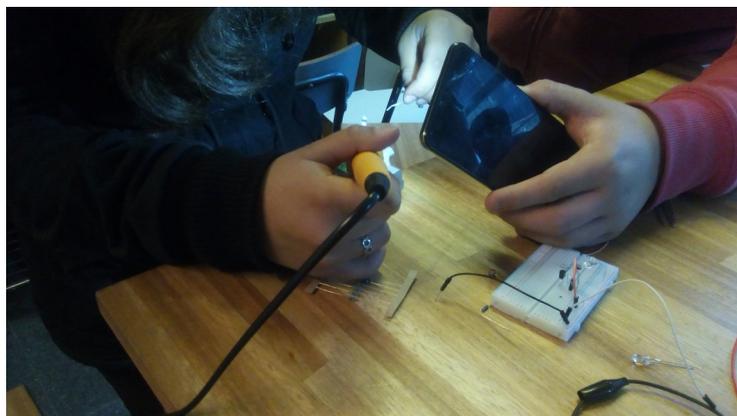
Placas, cables y soldadores. Taller 3. B. Fuente propia.
